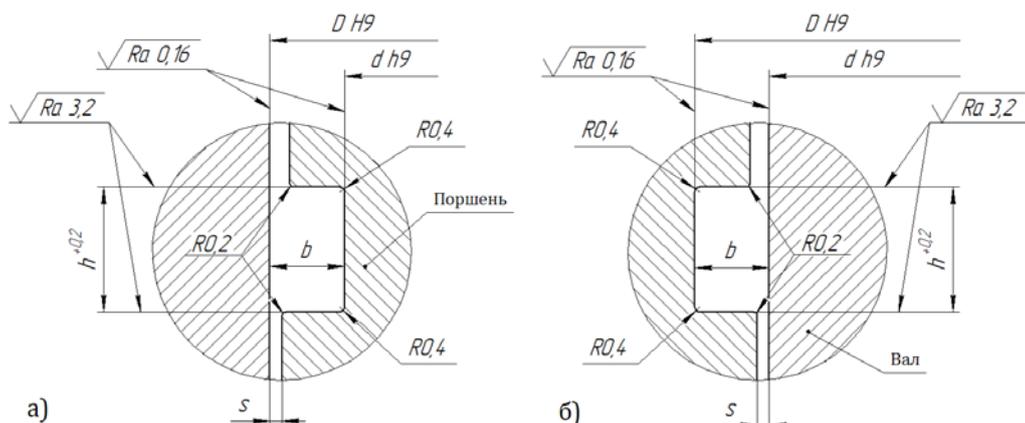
Закрытые канавки для уплотнения: а – поршня, б – штока
